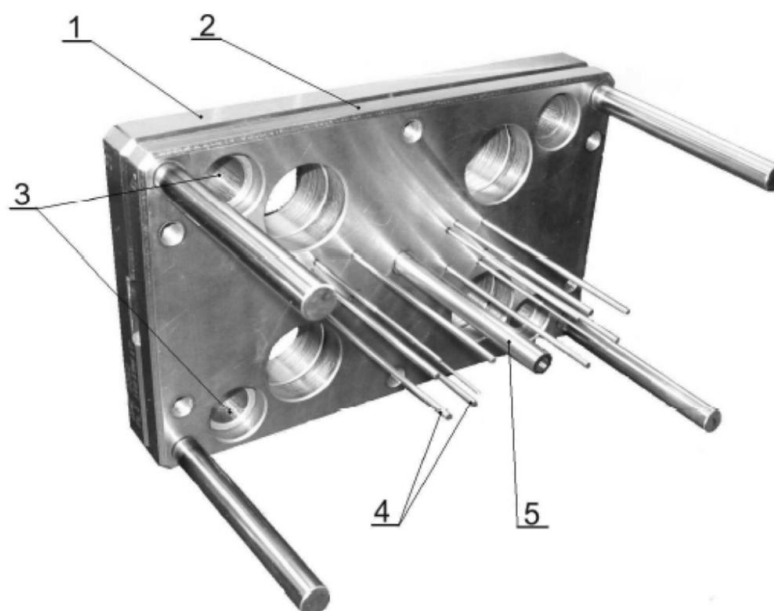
Ocelová deska s vyfrézovanými chladicími kanály – 4D integrat.[17]
